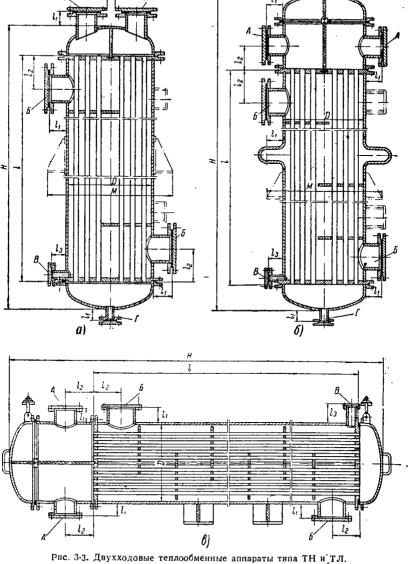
Двухходовые теплообменные аппараты типа ТН и ТЛ. а—типа ТН с двумя эллиптическими крышками; б—типа ТЛ с одной сварной и одной эллиптической крышками; в—горизонтальный типа ТН с одной камерной сварной и одной эллиптической крышками.
